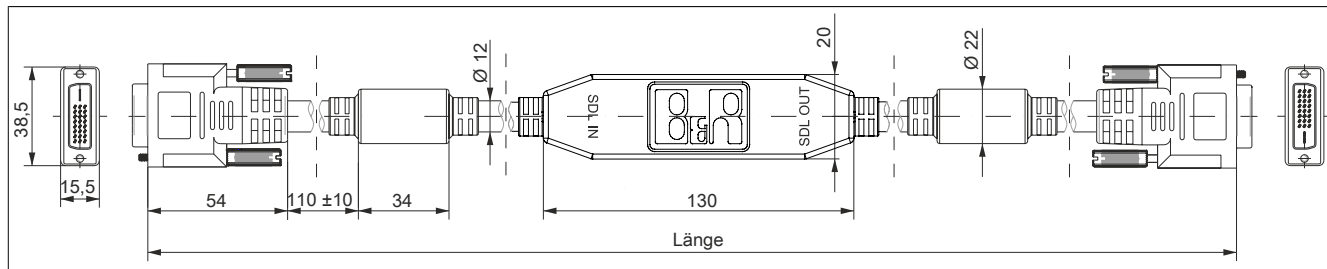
5CASDL.xxxx-13 ≥ Rev. E0 - Abmessungen
